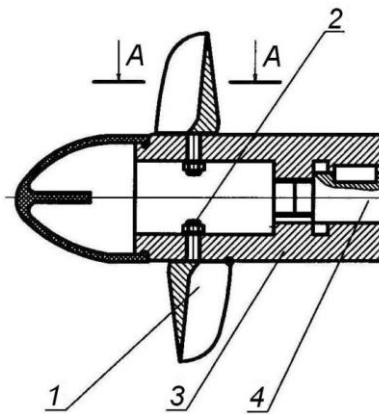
Рабочее колесо осевой гидротурбины в разрезе
